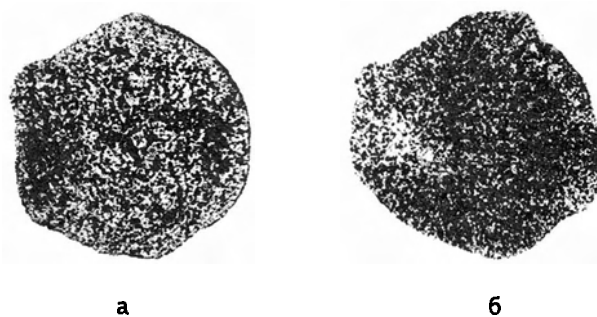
Макроструктура поперечных темплетов готового арматурного профиля №10, прокатанного из композиционной заготовки из стали 35ГС с разделением: а и б - разделенные профили, полученные из одной заготовки.
